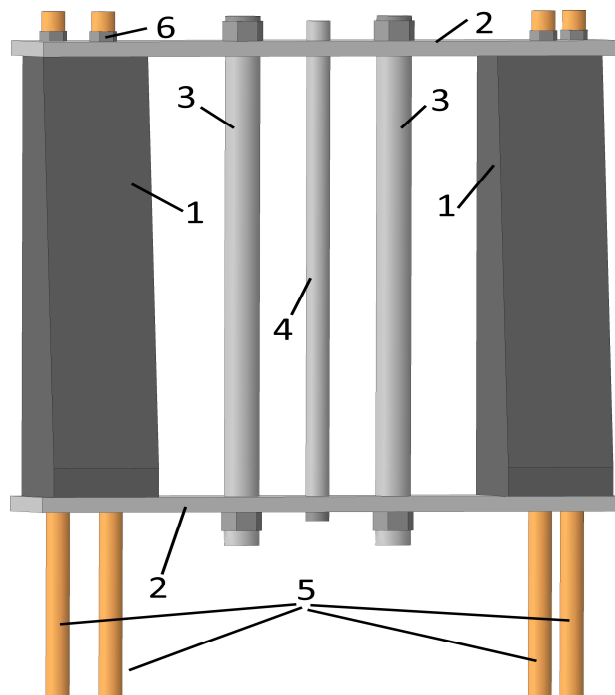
Вариант исполнения композитных стоек с армированием упруго-растянутыми шпильками
